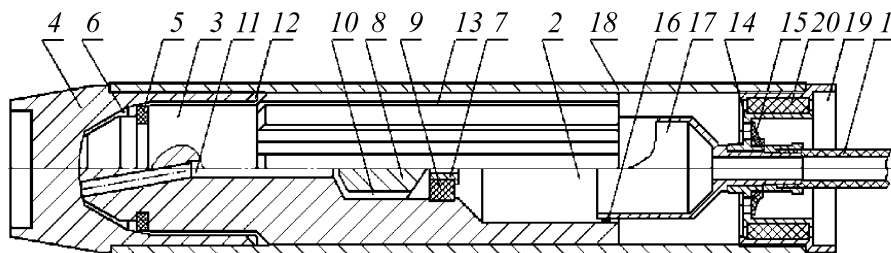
Устройство пневмомолота: 1 — рукав; 2 — камера прямого хода; 3 — ударник; 4 — наковальня; 5 — резиновое кольцо; 6 — камера обратного хода; 7 — жиклер с калиброванным отверстием; 8 — инерционный клапан; 9 — резиновое седло клапана; 10, 11 — каналы; 12 — пазы для выхлопа; 13 — канал; 14 — ступица; 15 — клапан; 16 — полиэтиленовое кольцо; 17 — патрубок; 18 — корпус; 19 — хвостовик; 20 — амортизатор
